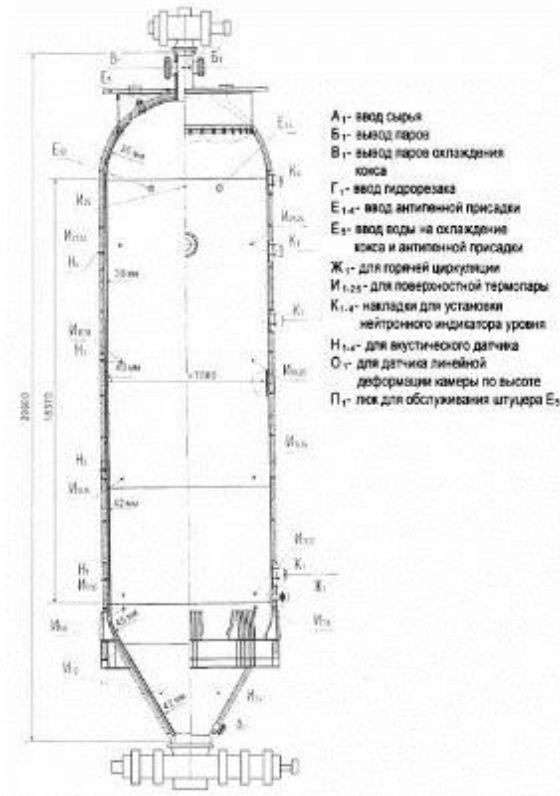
Чертеж коксовой камеры с боковым вводом сырья, направленным перпендикулярно к образующей конусной части [154]
